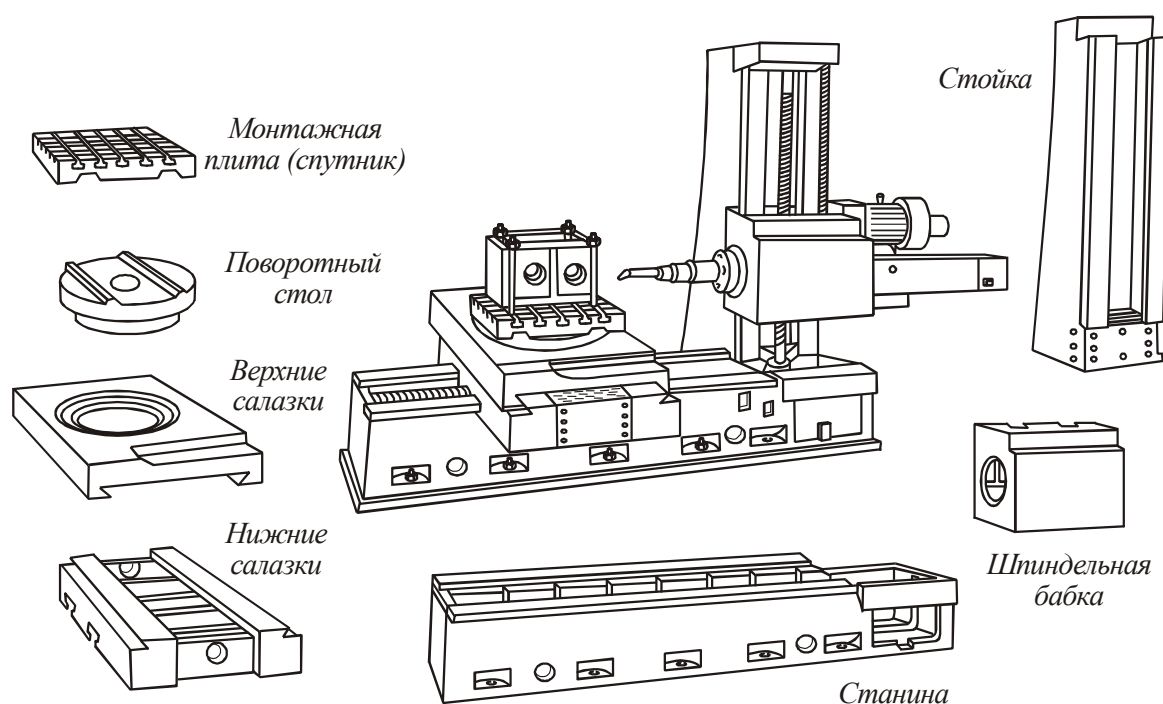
Базовые узлы и детали фрезерно – расточного станка
